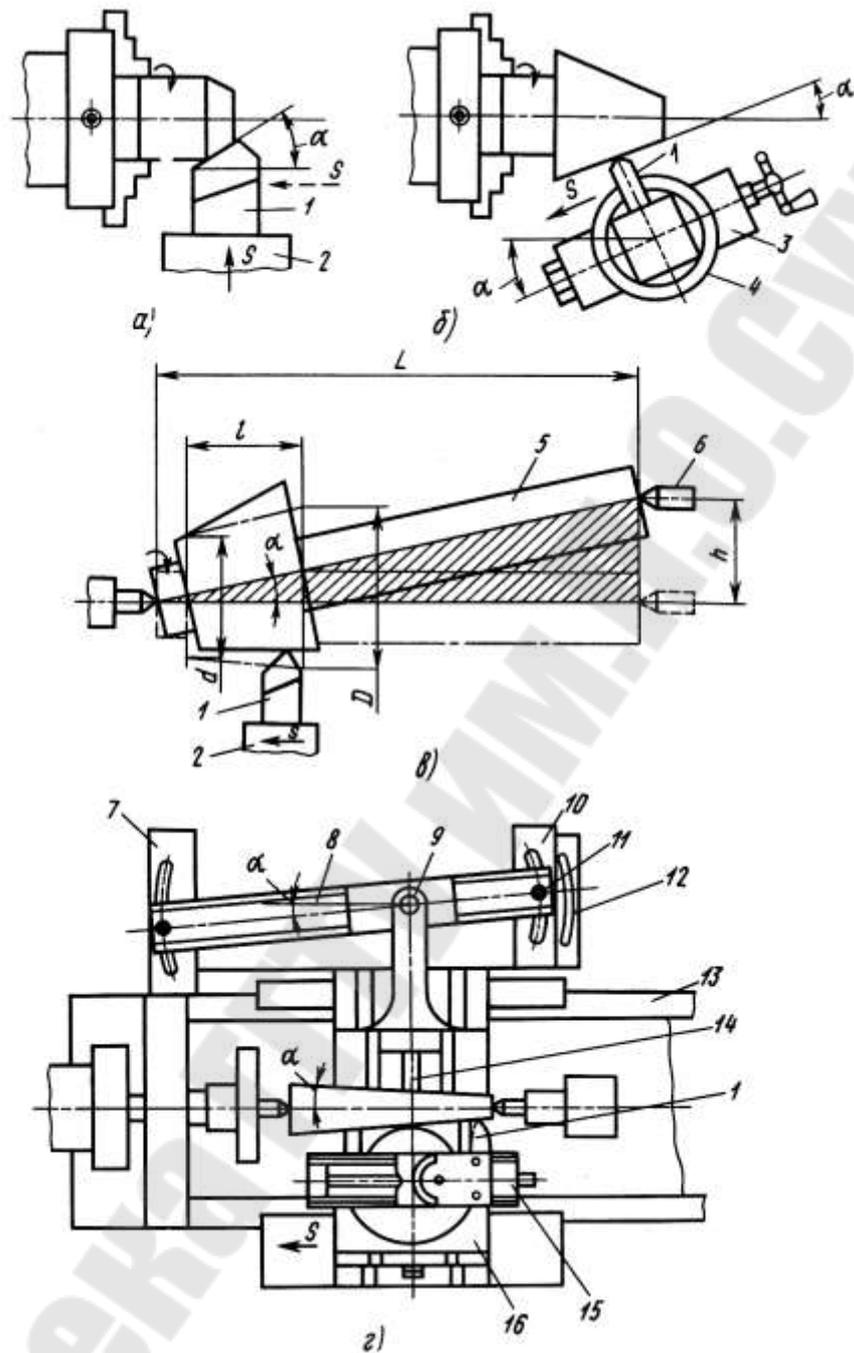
Схемы обработки конических поверхностей на токарно-винторезных станках:
